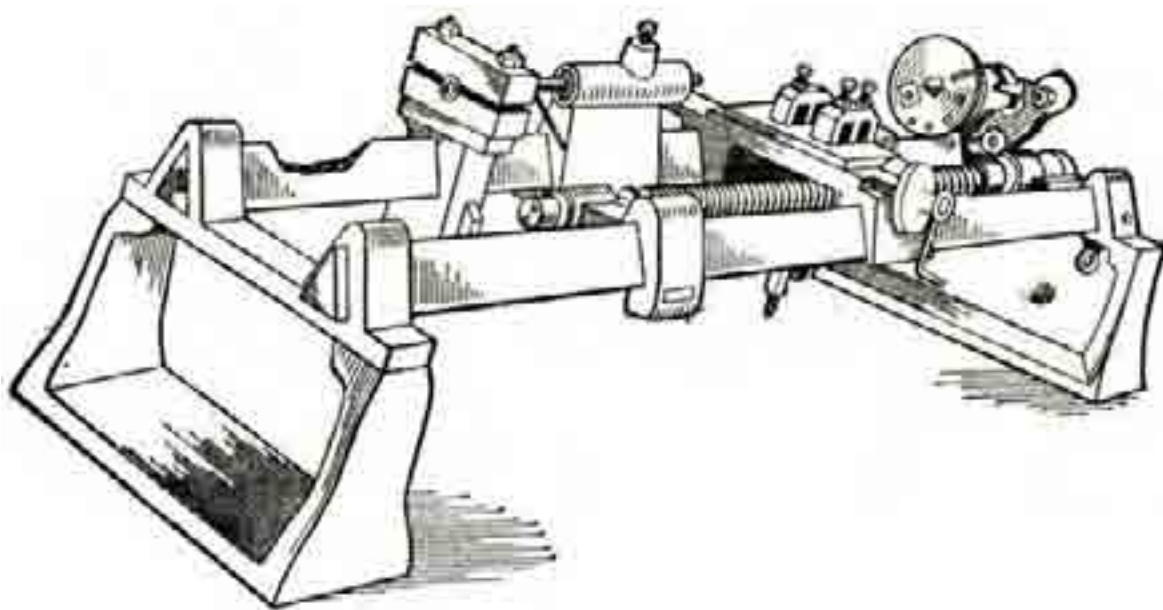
Токарно-винторезный станок Модсли 1800 г. с характерными закруглёнными формами
